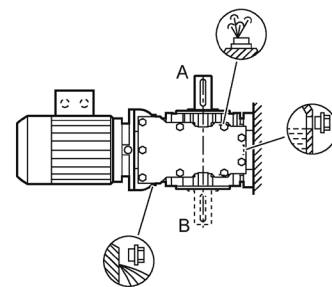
Einbautagen für Stirradschneckengetriebe C. Fußausführung Baugröße 39A
